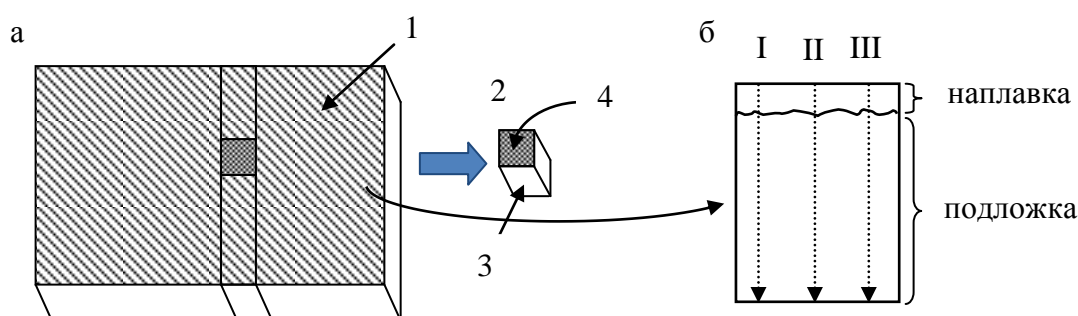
Схемы резки (а) и измерения микротвердости (б) по поперечному сечению образцов. 1 – подложка с наплавленной порошковой смесью; 2 – образец для исследований; 3 – поверхность образца для измерения микротвердости и металлографических исследований; 4 – поверхность образца для определения элементного состава; I, II, III – линии, вдоль которых измерялась микротвердость
